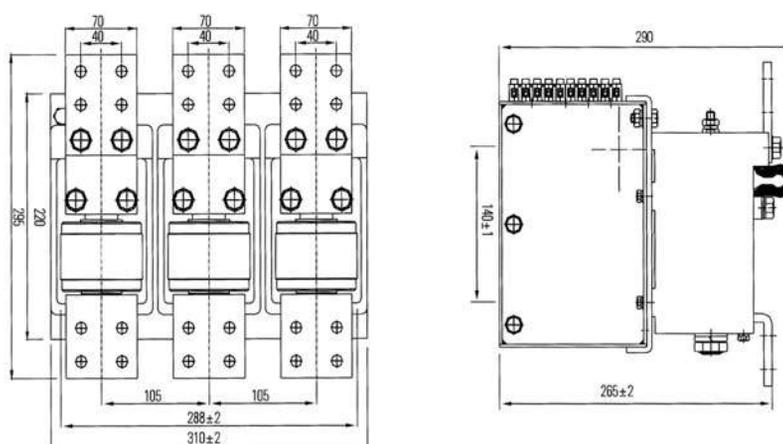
Габаритные размеры КВТ-1,14-1000/1250
